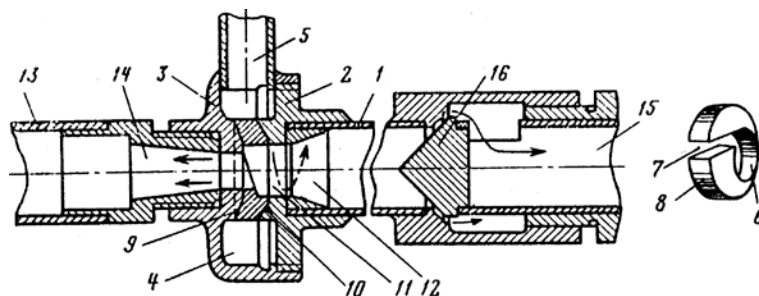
Конструкція циліндричної вихрової труби [5]
